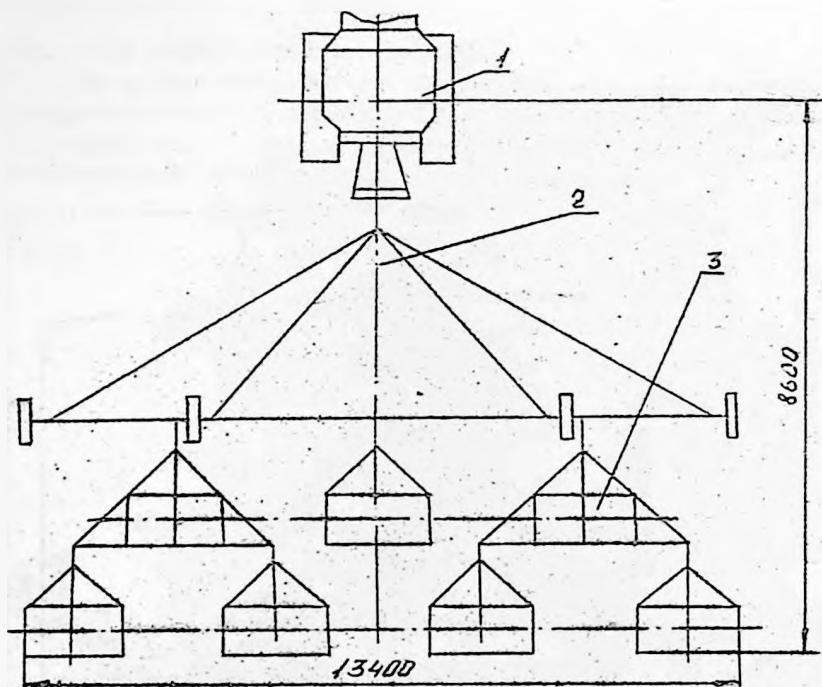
Схема агрегата с трактором МТЗ-80 для прикатывания почвы
